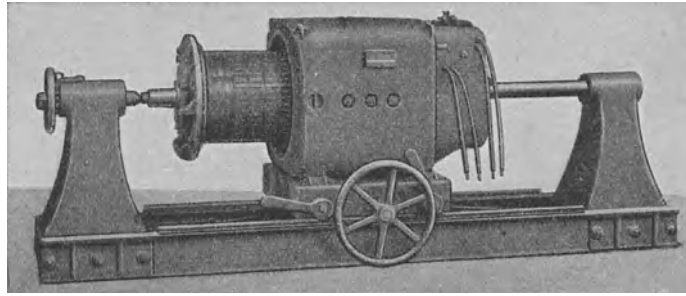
Spindelstock zum Herausnehmen des Ankers aus einem Motor mit einteiligem Kastengehäuse.
